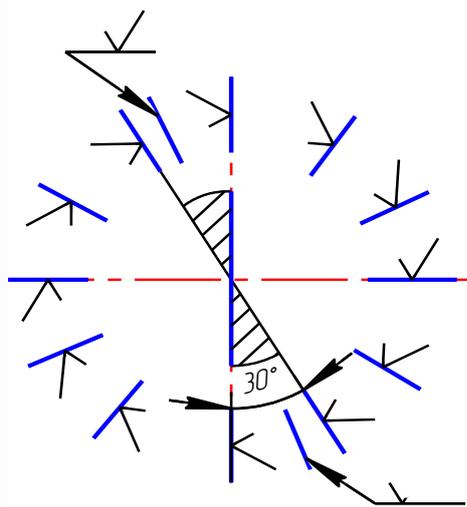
Расположение знака обозначения шероховатости без полки, относительно основной надписи чертежа [21]
